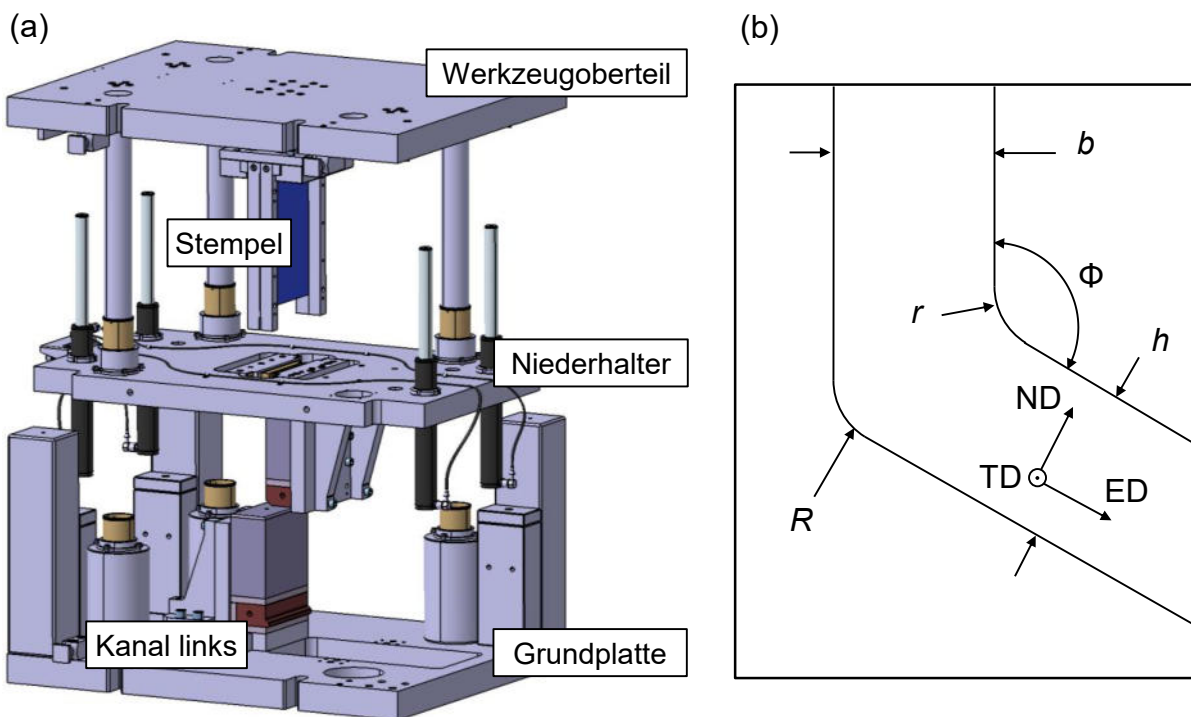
(a) ECAP-Werkzeug zur Bearbeitung von Blechwerkstoffen ab einer Blechstärke von 1,8 mm; (b) geometrische Parameter des ECAP-Werkzeugs für Blechwerkstoffe nach (Suh et al., 2015).
